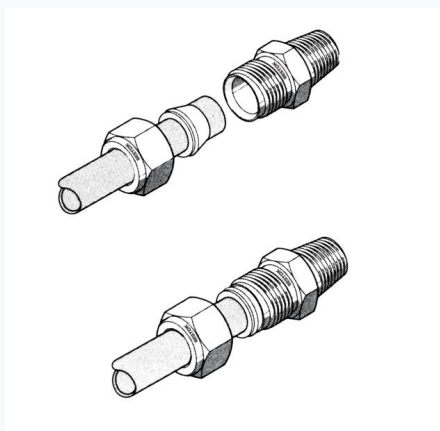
Установка предварительно обжатую сборку в корпус фитинга
